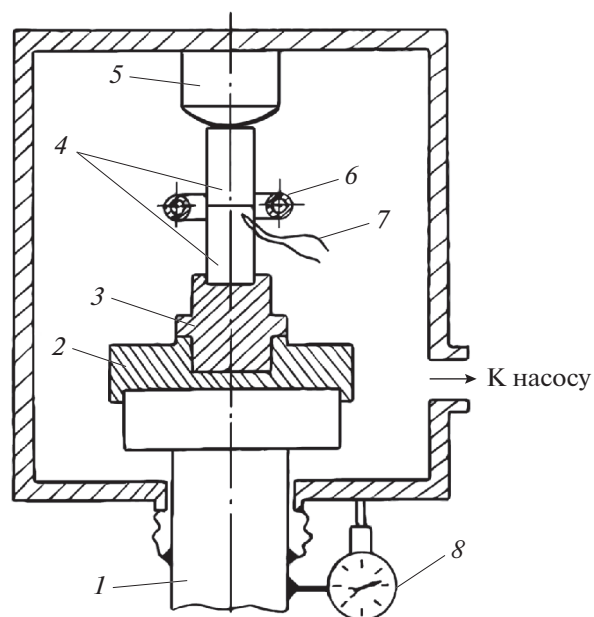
Схема установки для диффузионной сварки: 1, 5 – нижний (подвижный) и верхний штоки вакуумной камеры соответственно; 2 – центрирующий фланец; 3 – вкладыш (сменный); 4 – свариваемые керамические образцы; 6 – индуктор; 7 – термопара; 8 – индикатор.
